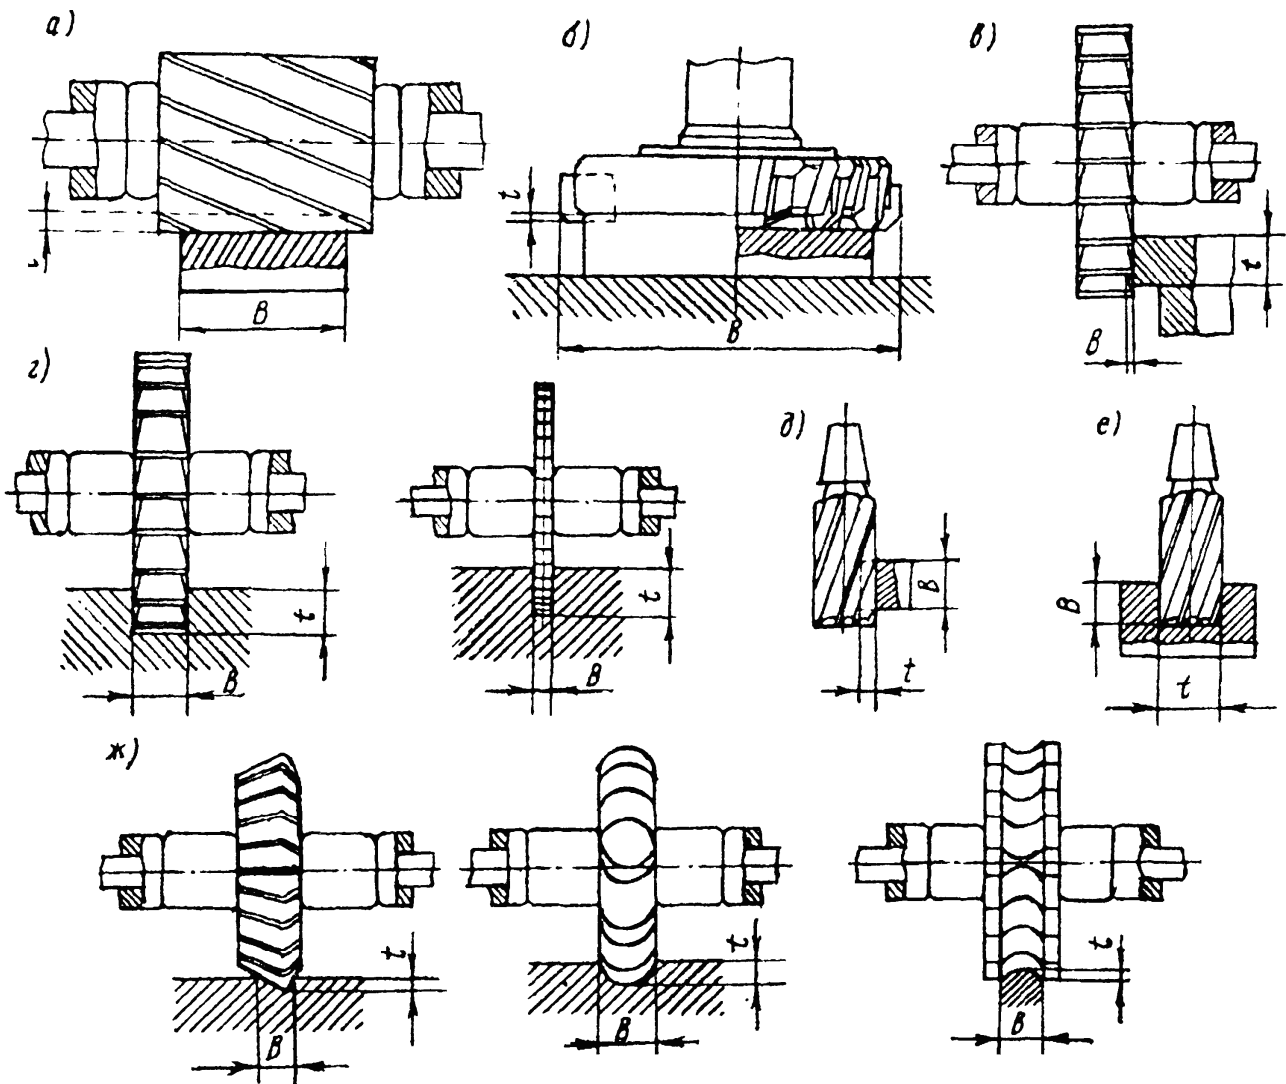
Основні схеми при фрезерних роботах: а) – обробка площини циліндричною фрезою; б) – те саме торцевою фрезою; в) – те саме дисковою фрезою; г) – фрезерування пазів дисковою фрезою; д) – обробка площини кінцевою фрезою; е) – фрезерування пазів кінцевою фрезою; ж) – фрезерування фасонними фрезами
